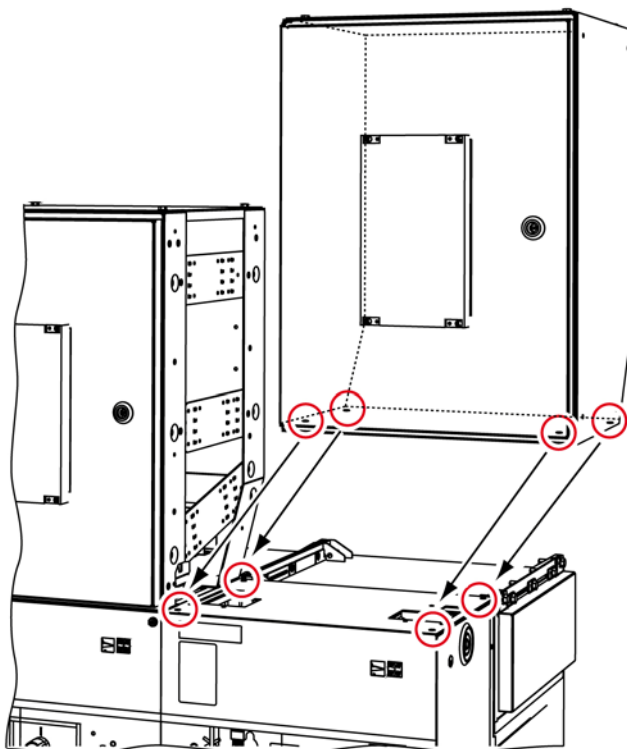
Крепление низковольтного блока к ячейке с помощью резьбовых соединений
